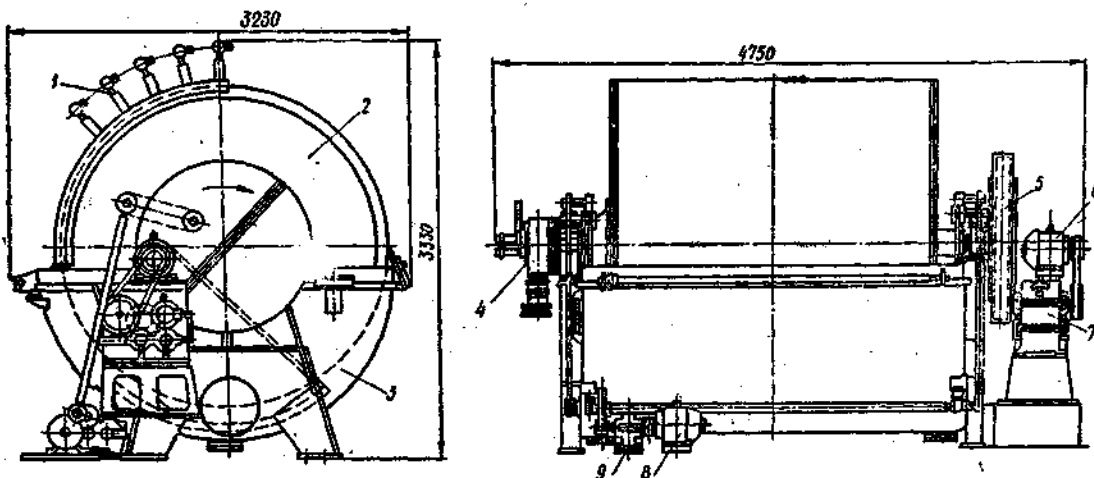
Барабанный вакуум-фильтр БОК20-2,6:
